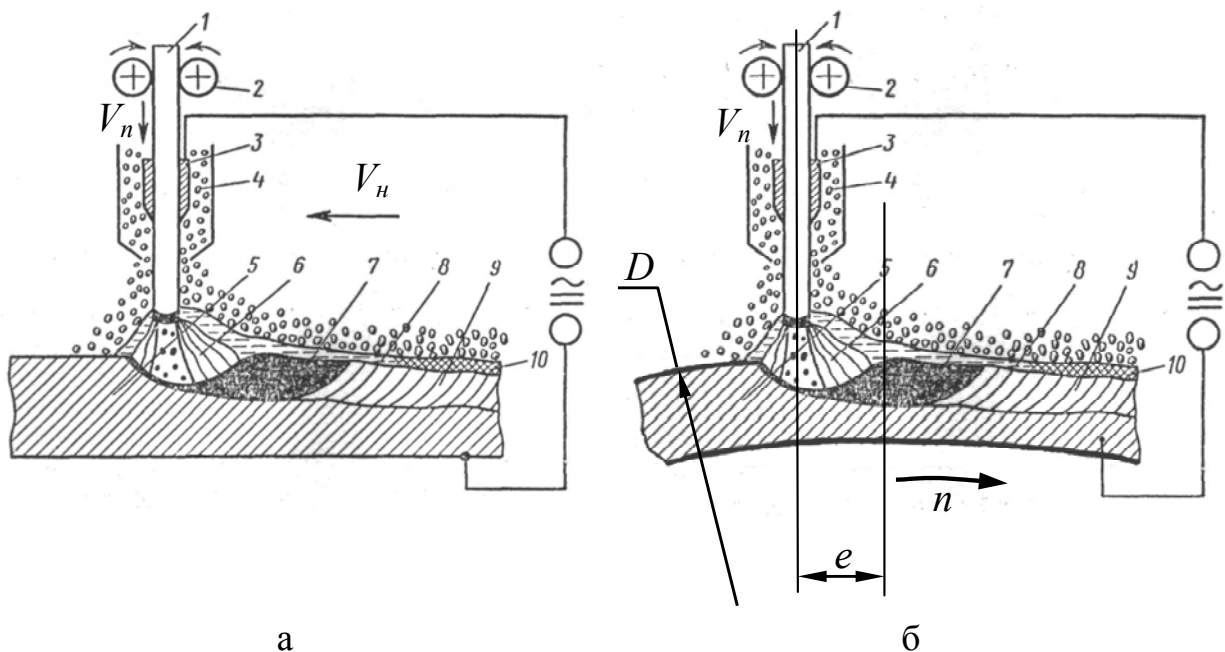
Схема автоматичного дугового зварювання під шаром флюсу прямолінійного шва (а) и кільцевого шва (б): 1 – електродний дріт; 2 – валики подавального пристрою; 3 – мундштук; 4 – флюс; 5 – деталі, що зварюються; 6 – дуга; 7 – розплавлений метал; 8 – розплавлений флюс; 9 – зварювальний шов; 10 – кірка
